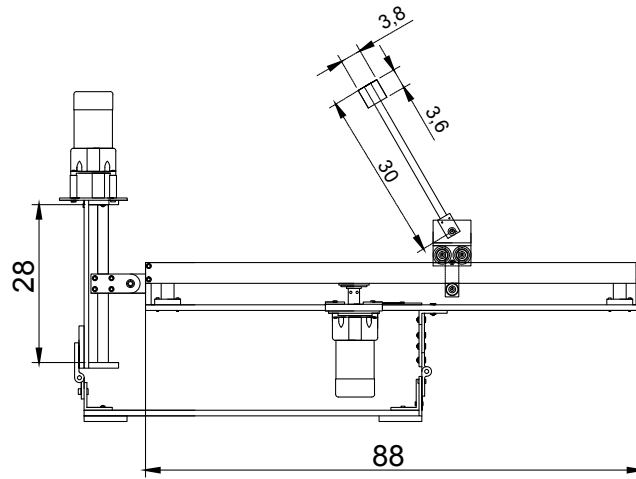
Plano frontal de la planta del Péndulo Invertido Simple - UV
